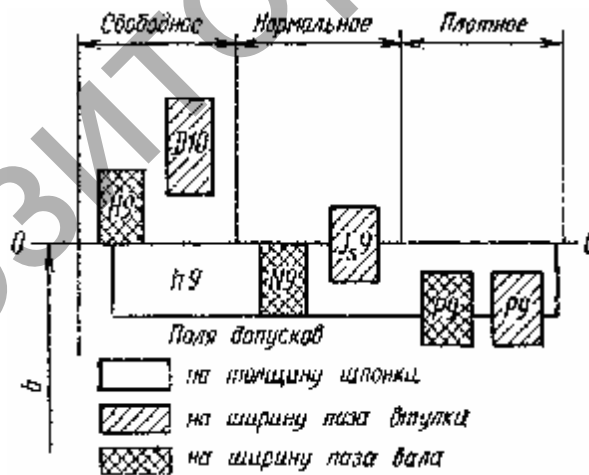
Поля допусков с призматическими шпонками
